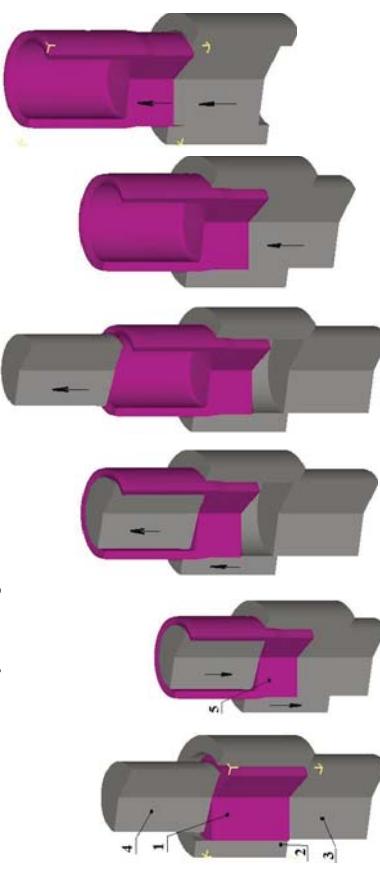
Розрахункові схеми в розрізі для ЗВР заготовки діаметром $D_o = 50$ мм
